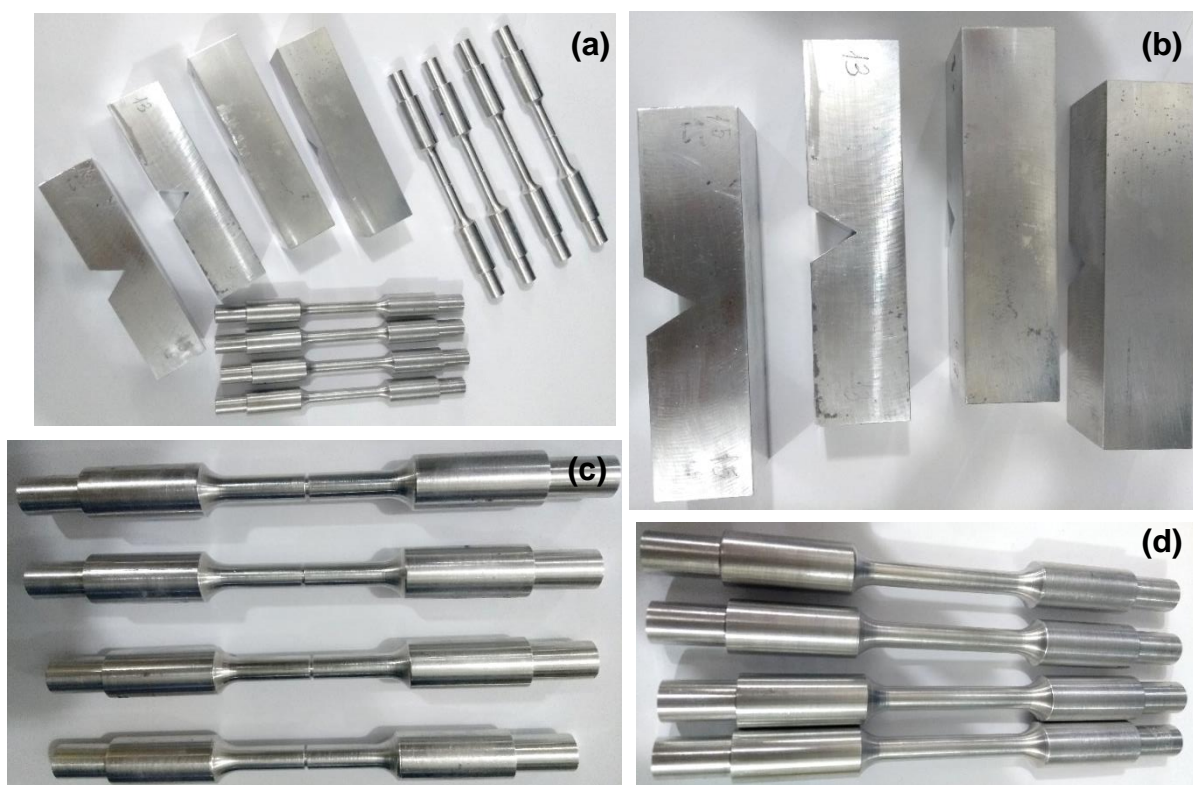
Corpos de prova usinados (a), detalhes dos corpos de prova de flexão com entalhe (b), tração com entalhe (c) e tração sem entalhe (d).
